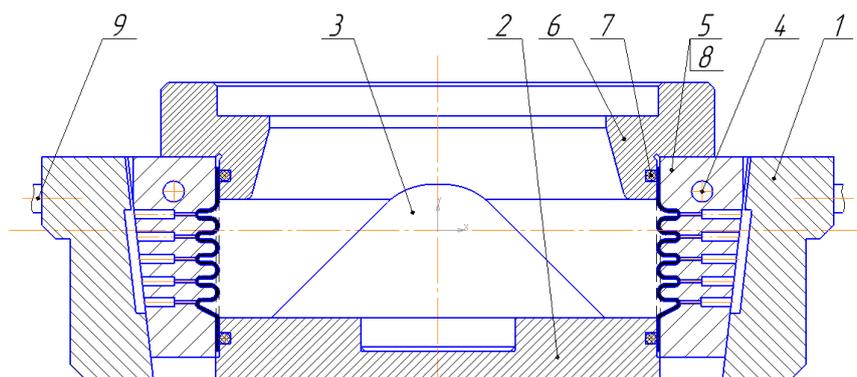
Чертеж штампа для взрывной штамповки: 1 – Бандаж; 2 – Вкладыш; 3 – Палец распределительный; 4 – Ловитель; 5 – Матрица; 6 – Фланец; 7 – Уплотнение
